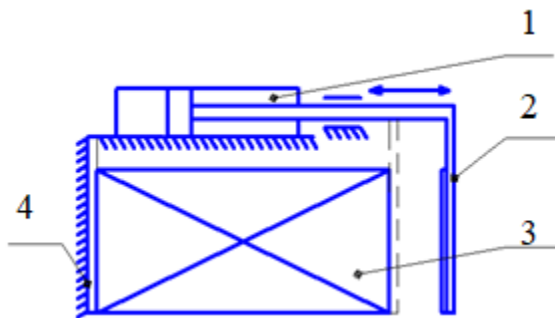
Схема механічного захоплювального пристрою з однією рухомою стулкою: 1- пневмоциліндр; 2 – рухома стулка; 3 – упаковка; 4 – опорна поверхня
